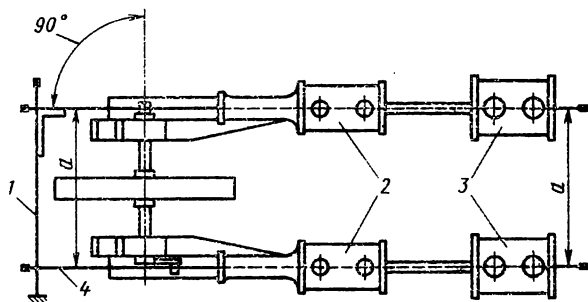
Схема проверки параллельности осей цилиндров спаренной паровой машины:
